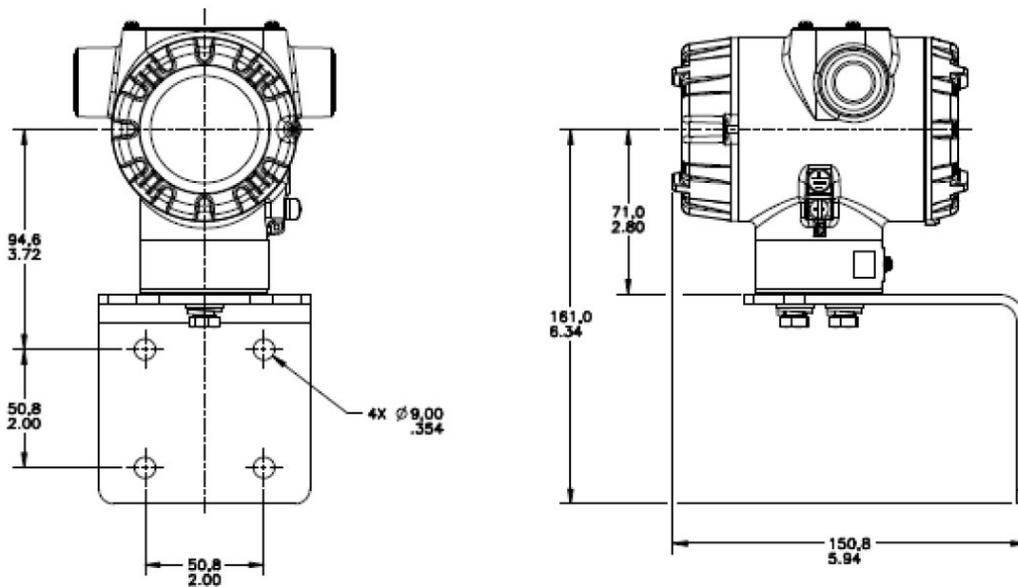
STT850 без адаптера. Монтаж на вертикальную трубу при помощи угловой монтажной скобы
